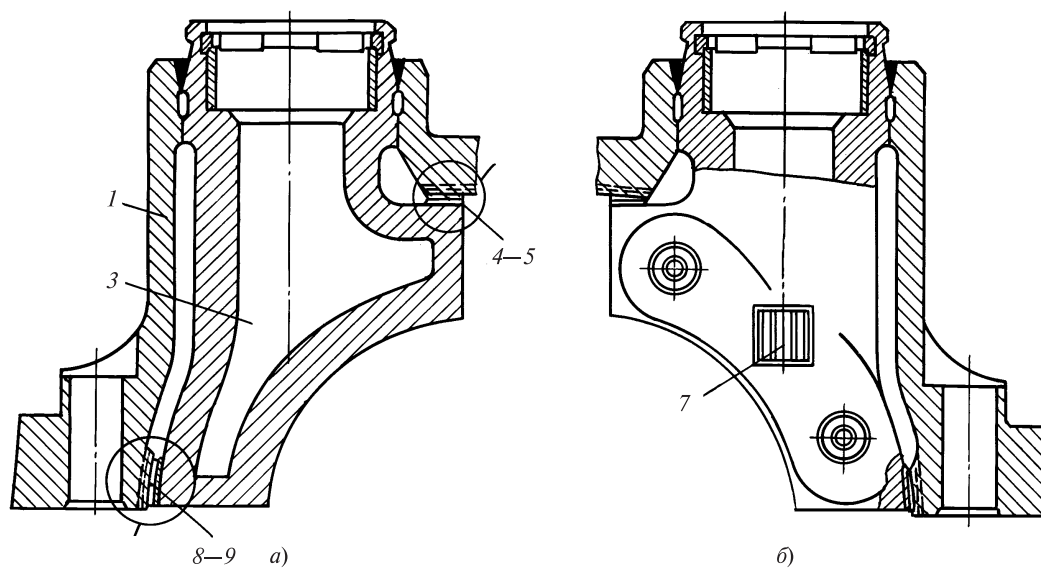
Двухстенный корпус ЦВД турбины Т-250/300-23,5 ТМЗ
